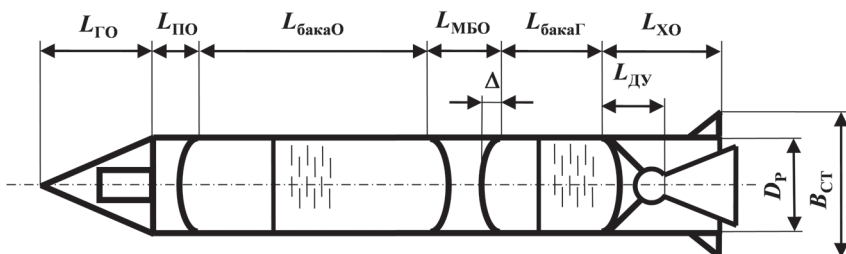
Конструктивно-компоновочная схема одноступенчатой ракеты с обозначением основных геометрических размеров
